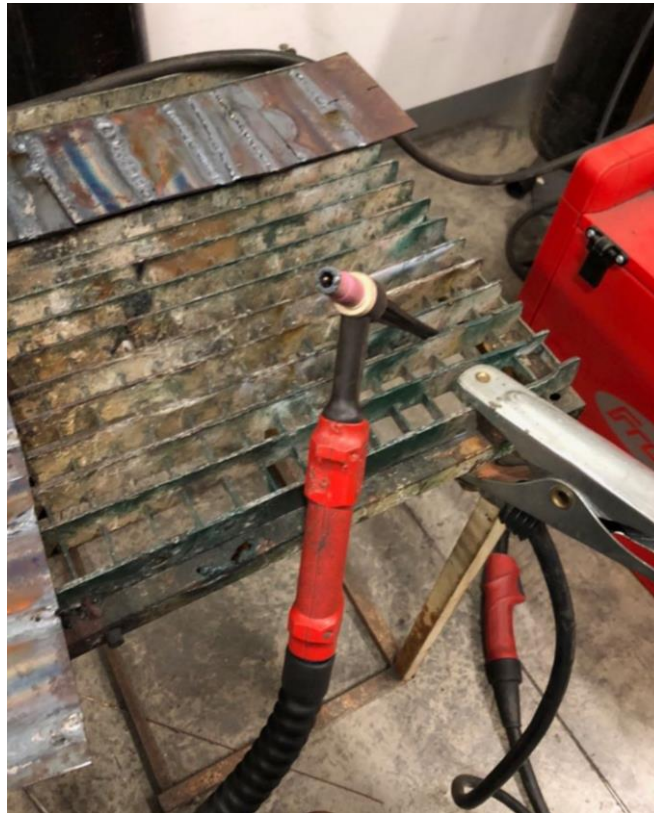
Equipo de soldadura empleado en este trabajo
